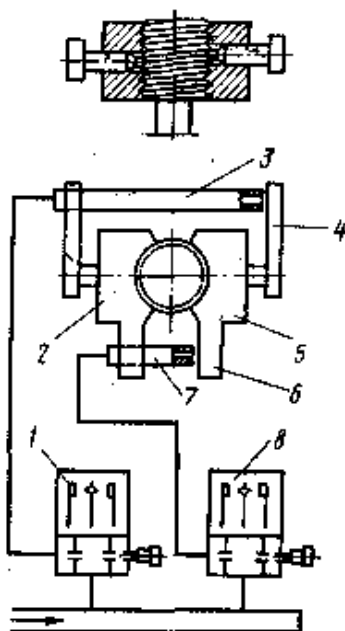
Метролргическая схема автомата БВ-538 для контроля резьбы корпусов запальных свечей
